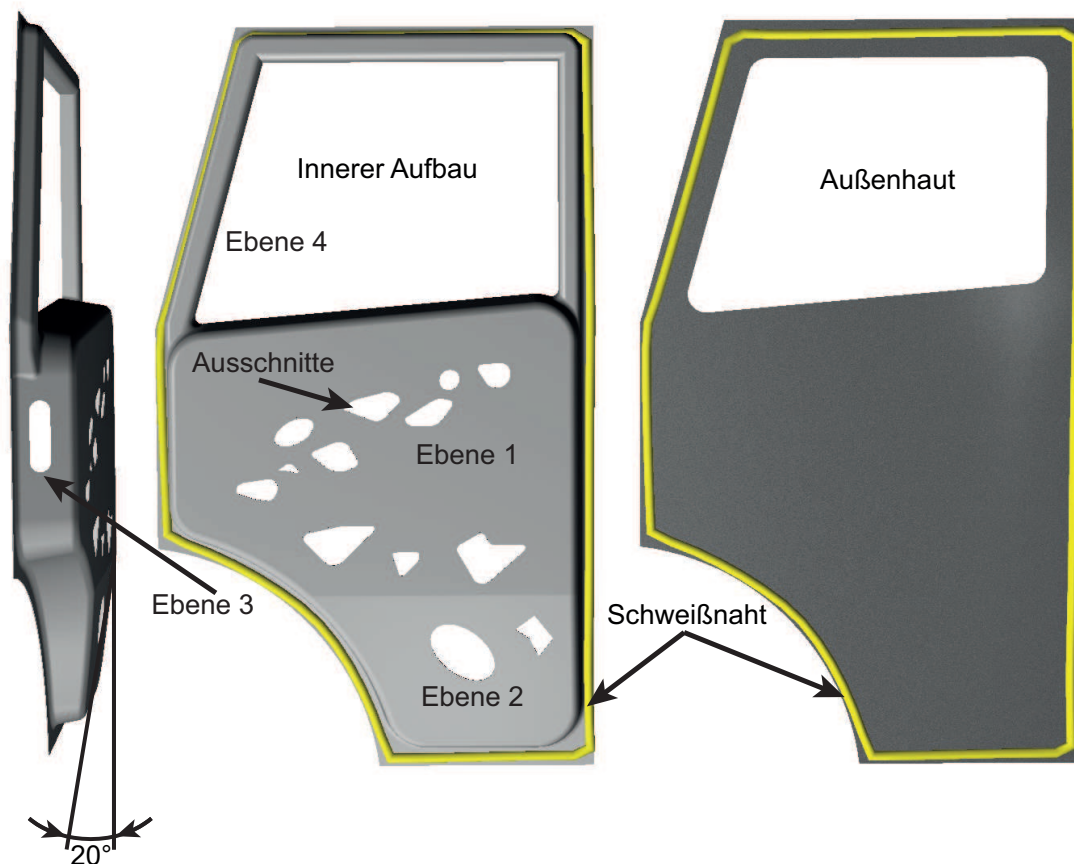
Versuchsbauteil LKW-Türe mit Ausschnitten und einer umlaufenden Schweißnaht
